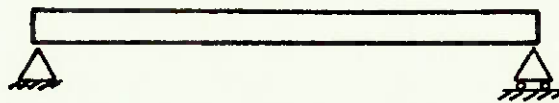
CONDIÇÕES DE APOIO DA CHAPA NA SOLDAGEM
